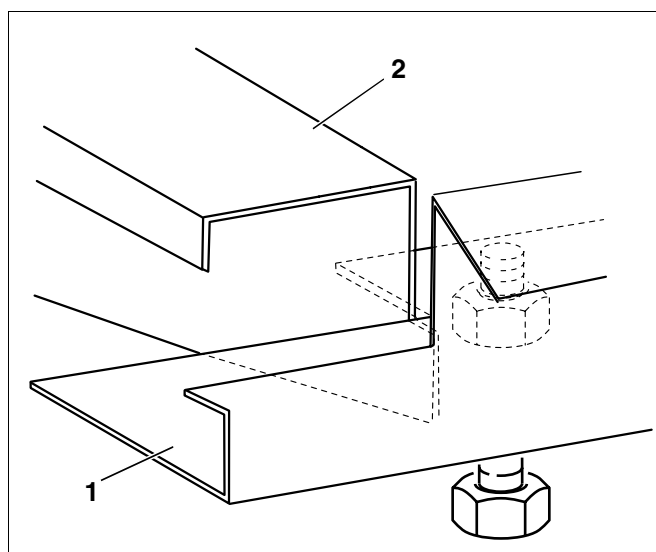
Poser la traverse longitudinale sur la traverse transversale
